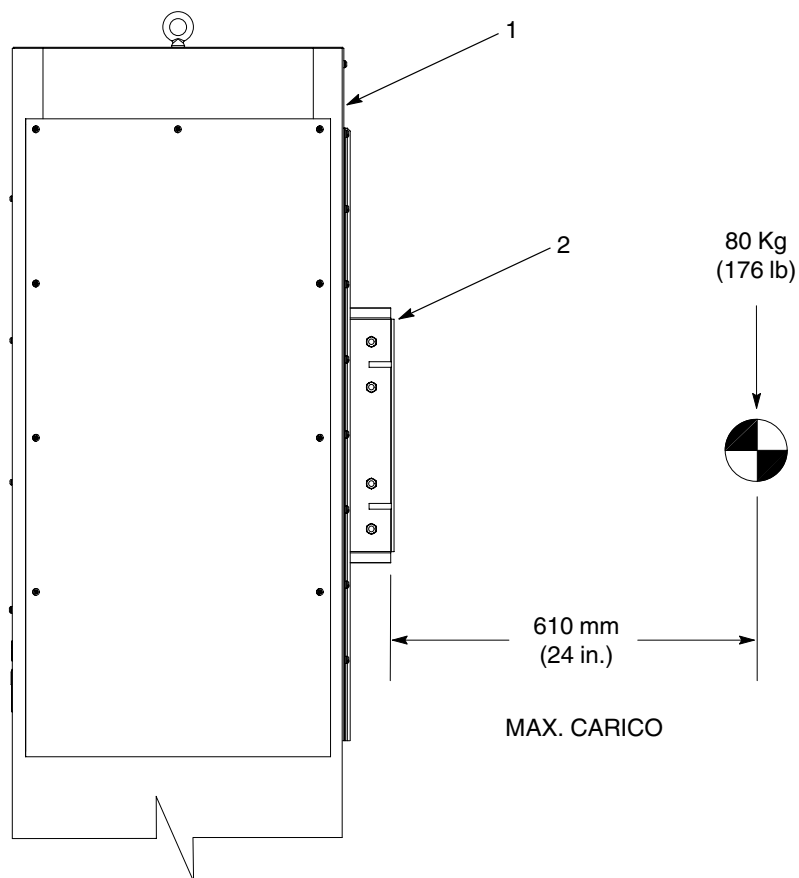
Installazione delle pistole e dei loro dispositivi di montaggio
